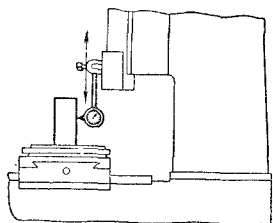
Проверка перпендикулярности направляющих консоли фрезерного станка с направляющим станины.
